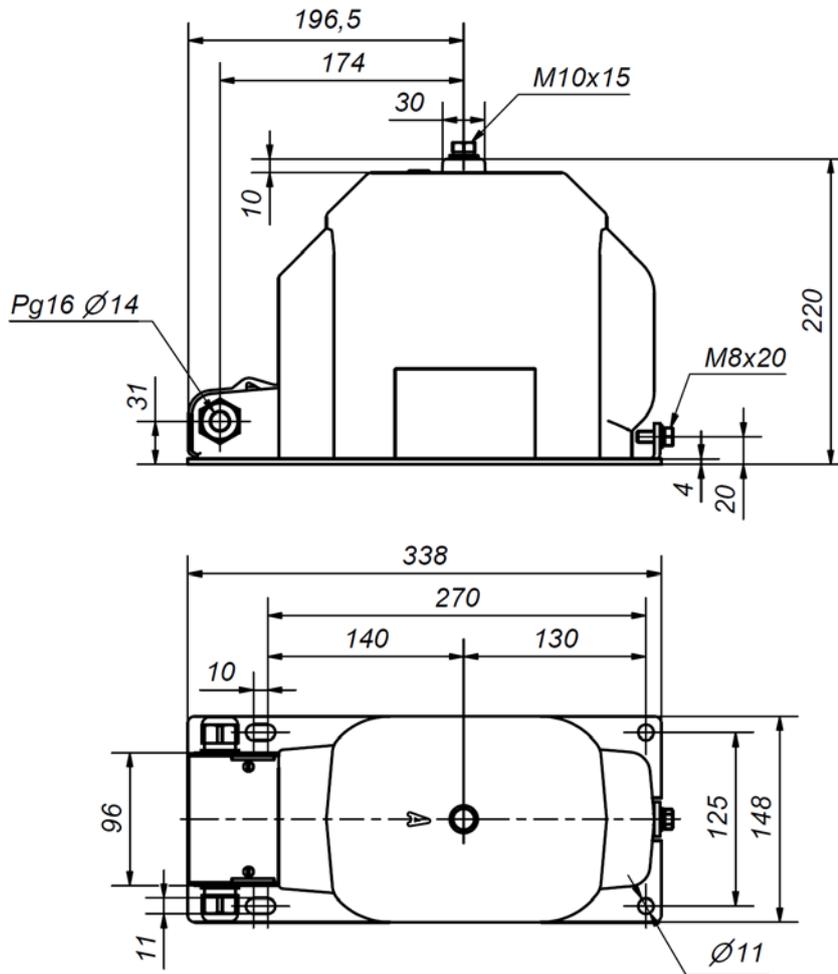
Габаритный чертеж трансформаторов IVS1-1.1.1...
